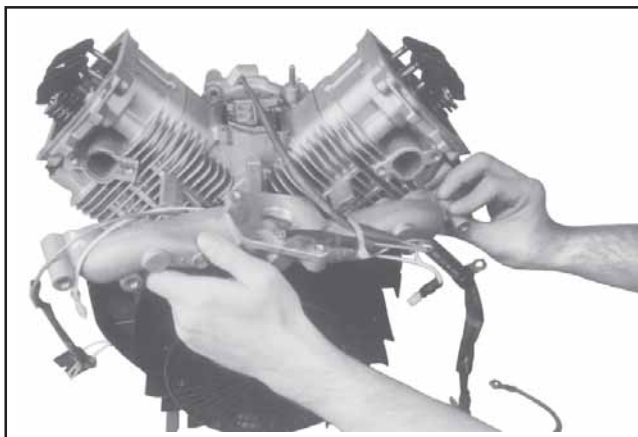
Installazione del collettore di aspirazione con il cablaggio (collettore in alluminio).
